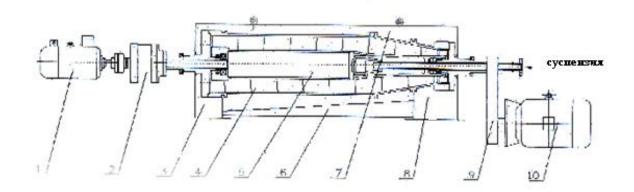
Принципы устройства 1 - вспомогательный двигатель (тормозное устройство, либо защитное устройство вращающего момента) 2 - дифференциальный механизм 3 — выходное отверстие для жидкости 4 - барабанят 5 - винтовой конвейер 6 - основа 7 - капот 8 — выходное отверстие для шлака 9 - привод 10 - основной двигатель
